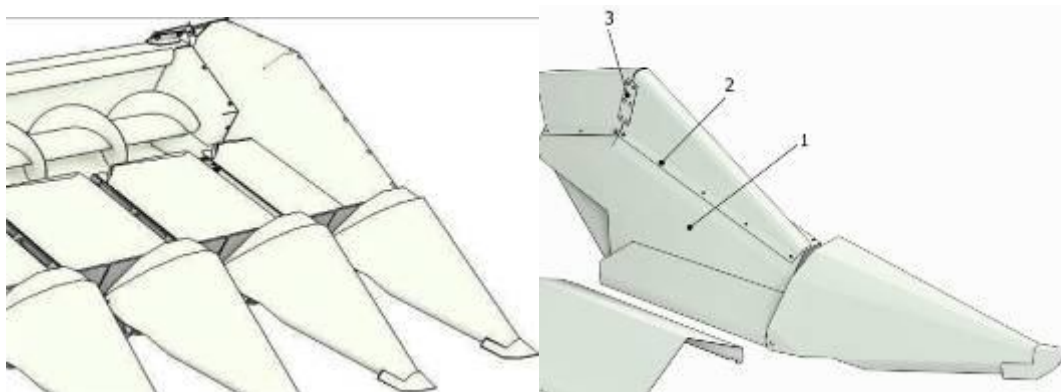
Боковые капоты серийного приспособления (слева) и жатки RSM MS-870-49 с дополнительными съемными щитами (справа):
